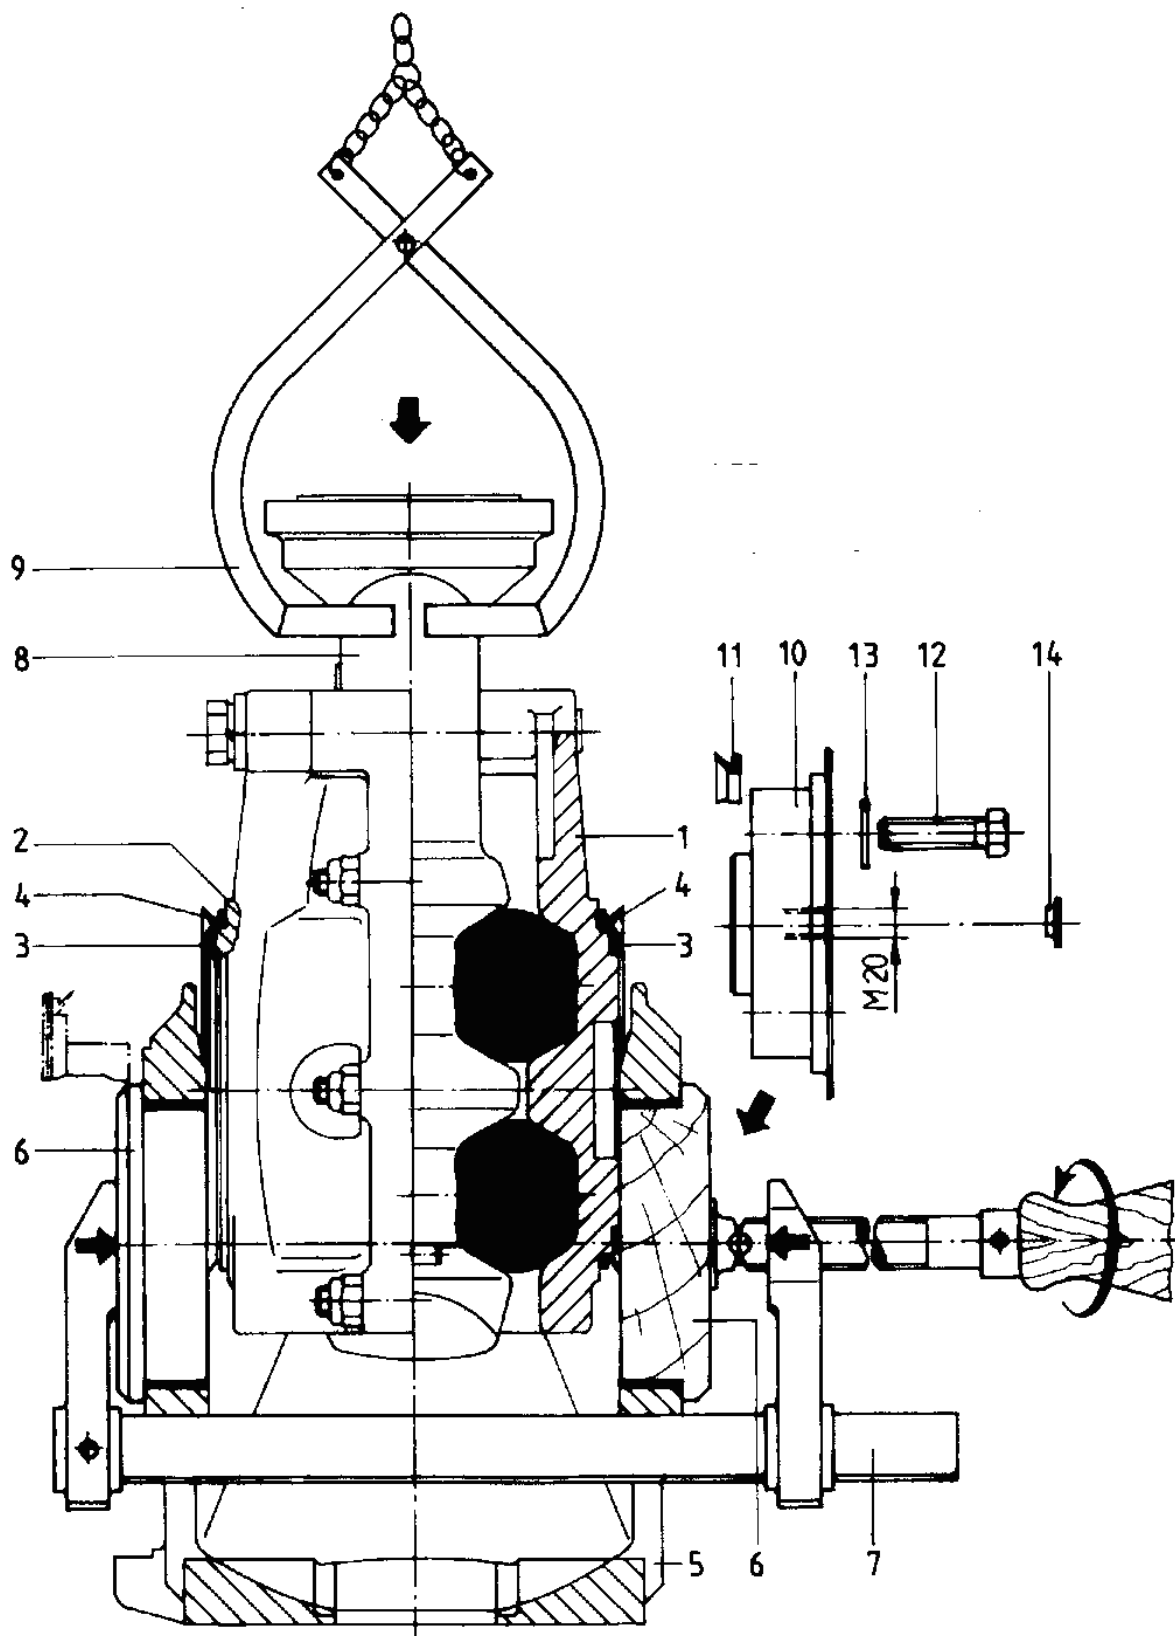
Montaje de la unidad de resortes del caballete – esquema de principio
